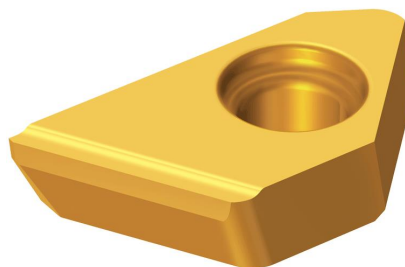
Твердосплавна ріжуча пластина з покриттям для обробки фасок з кутом 60°
